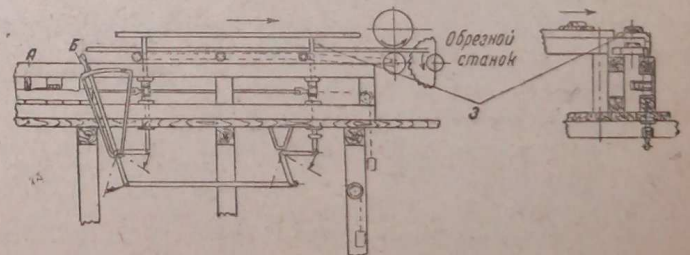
Приспособление для подготовки досок на столе перед обрезным станком:
